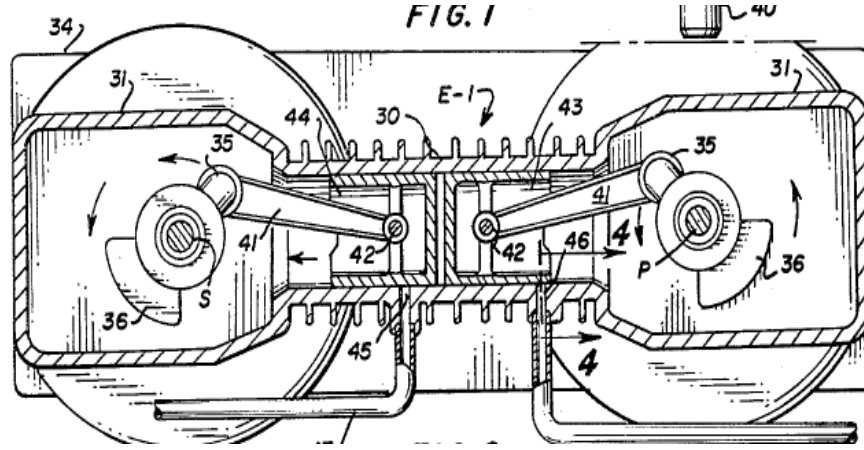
William. R. Erick karşıt pistonlu motoru [5].
